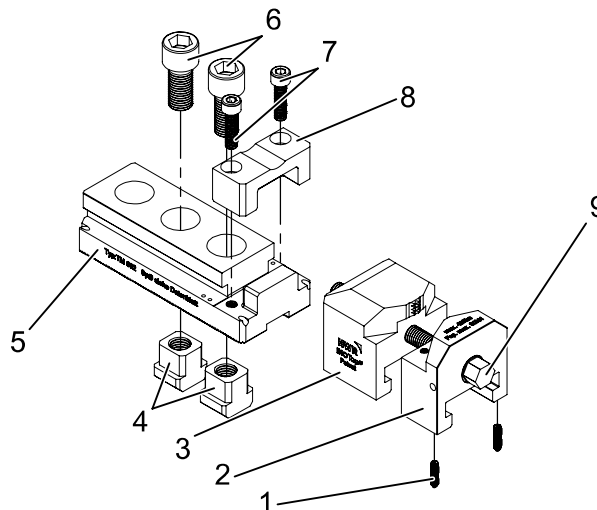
Montaggio delle ganasce di serraggio - mandrino di serraggio piccolo
